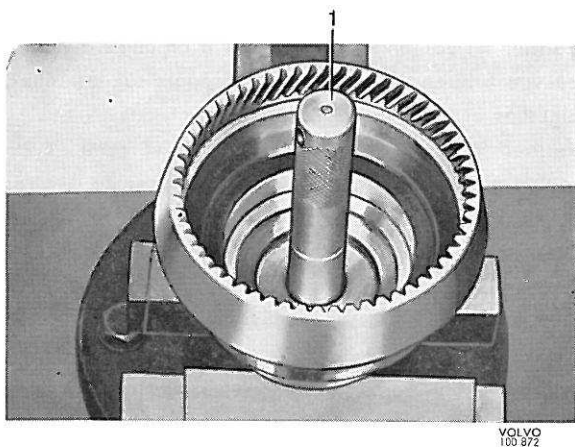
Remontage du roulement à aiguilles, arbre de sortie
